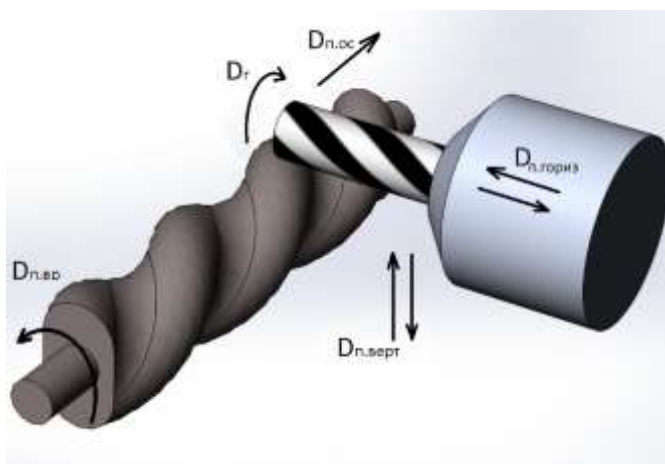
Схема обработки винтовой поверхности осевым инструментом на фрезерном станке с ЧПУ.
